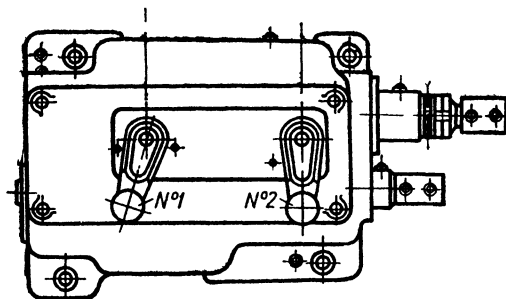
Внешний вид коробки подач токарно-винторезного станка модели 1615-М.
